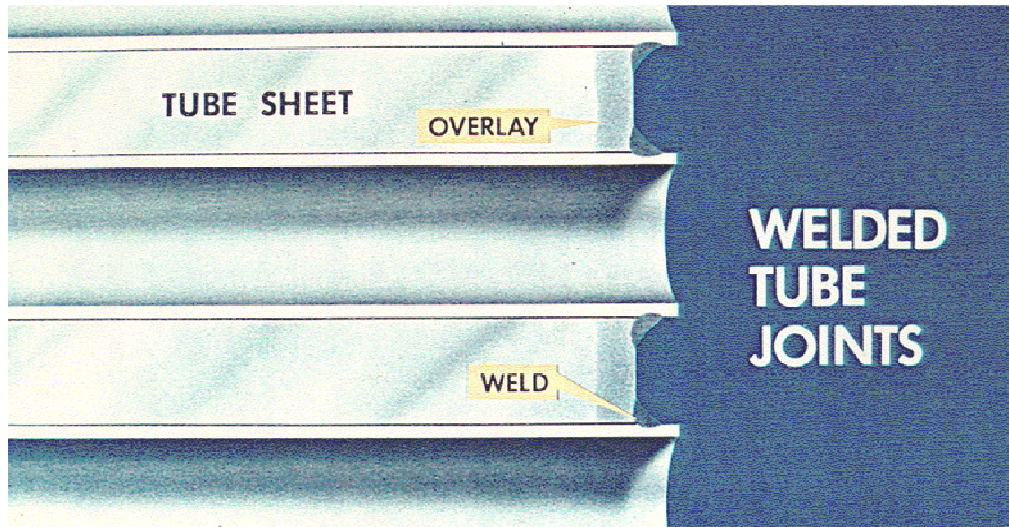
Detalle unión tubo/placa-tubular con recarga
